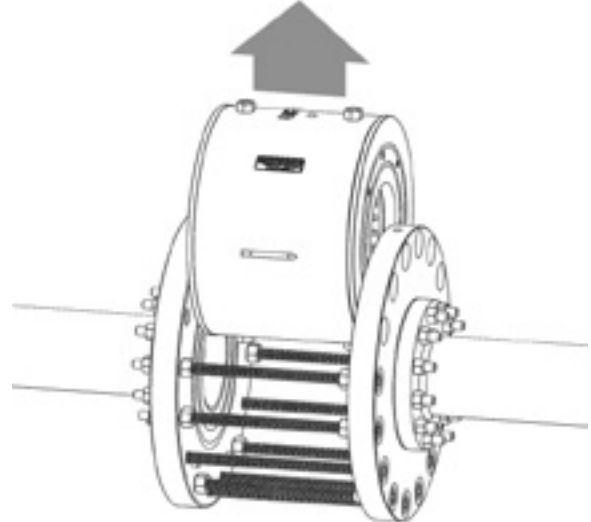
Heben Sie die Rumpfbaugruppe aus der Leitung.
